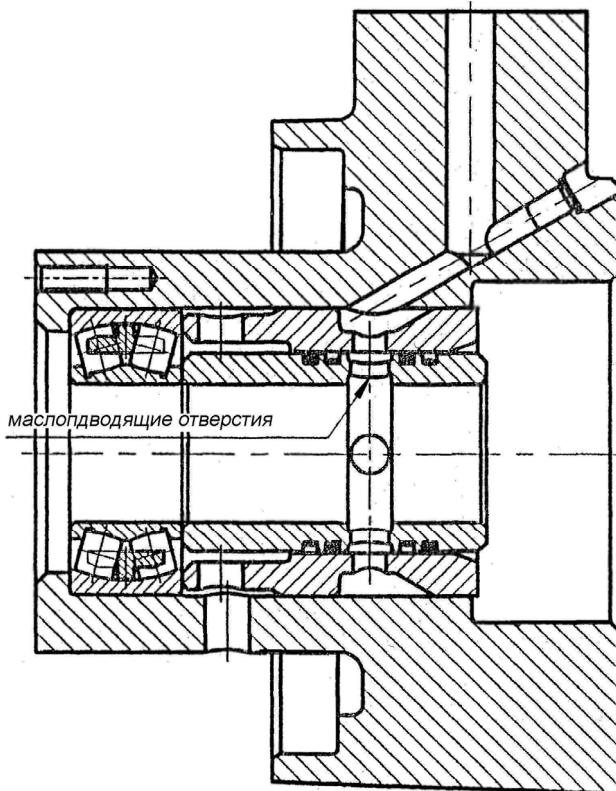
Установка распорных втулок в корпус привода вентилятора
